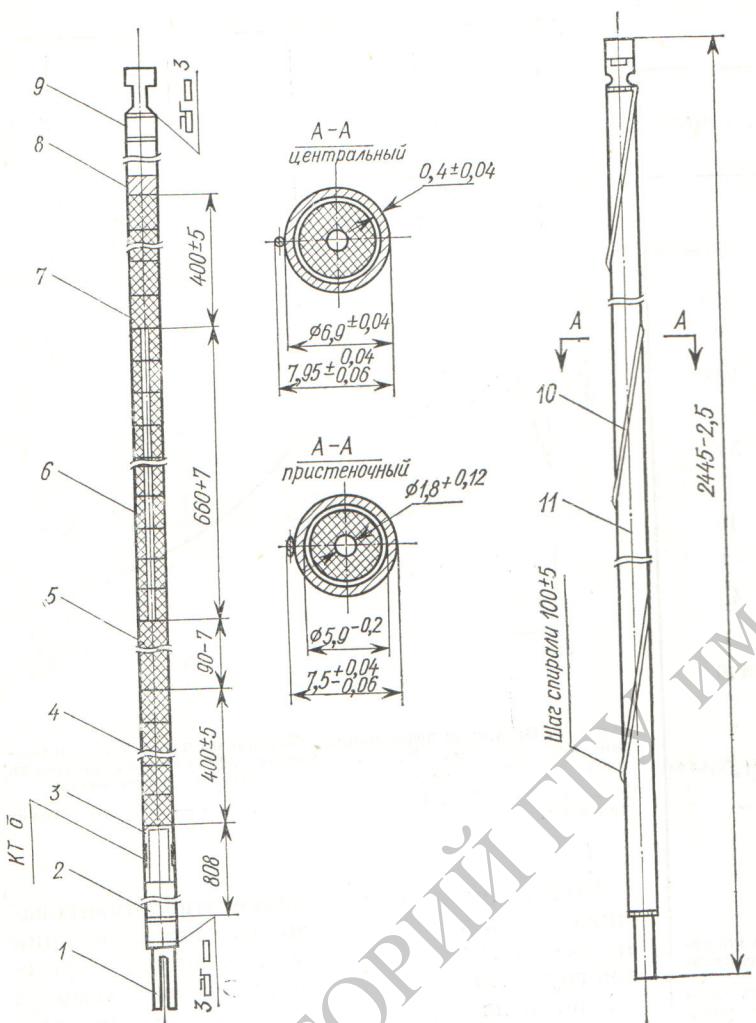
Вариант конструкции твэла активной зоны реактора БН-600:
